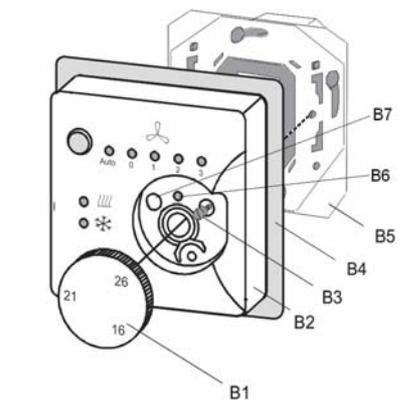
Montage des Fan-Coil Unit Bediengerätes
